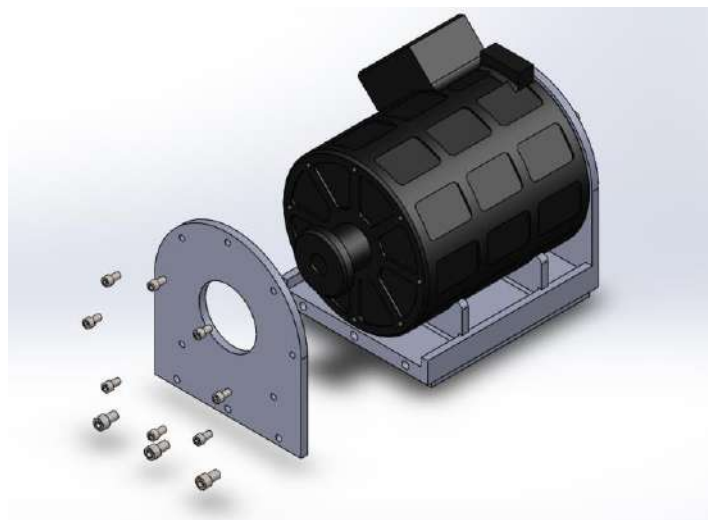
Assembly Motor dan Mounting Motor
